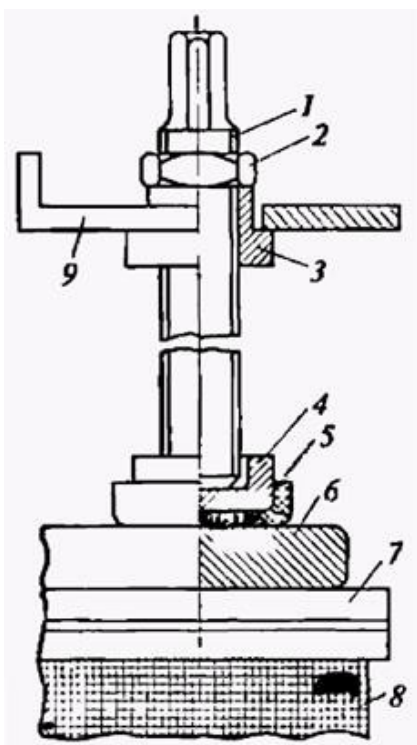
Осевая прессовка обмоток кольцами и нажимными винтами:
